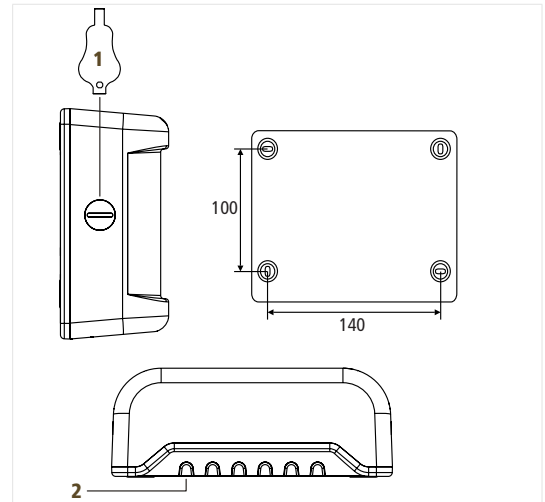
Abmessungen für Montagelöcher (Angaben in mm)
